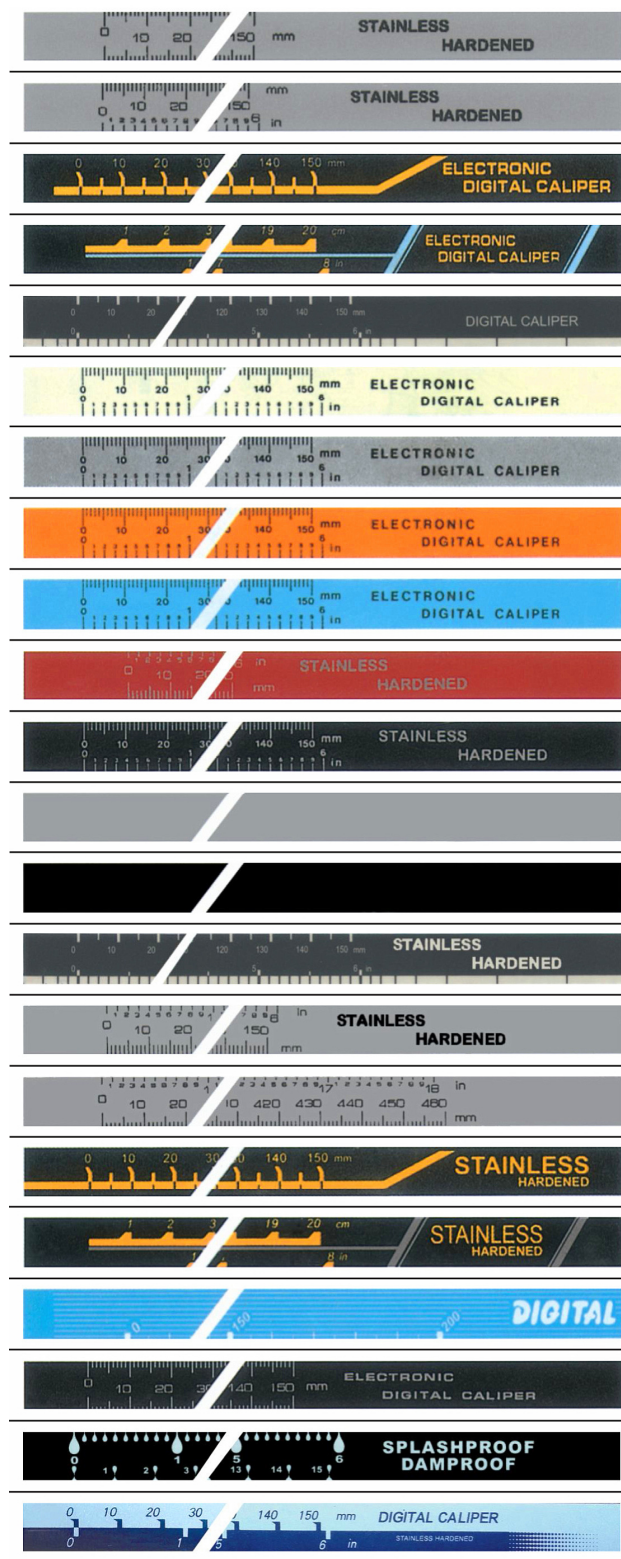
Варианты исполнений общего вида штанги штангенциркулей
